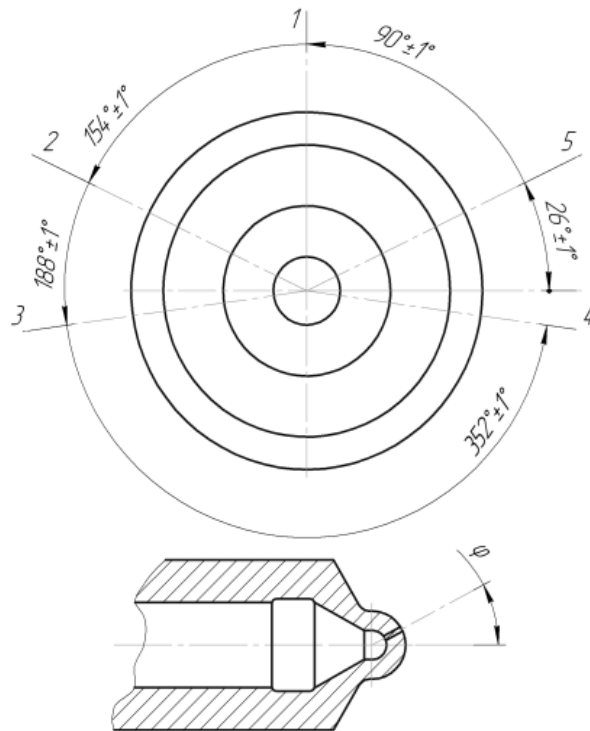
Схема розташування форсунки і циліндра двигуна 468А-1
